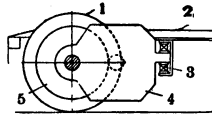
а: 1—ведущее колесо, 2—рама, 3—пружина, 4—двигатель, 5—большое зубчатое колесо.
